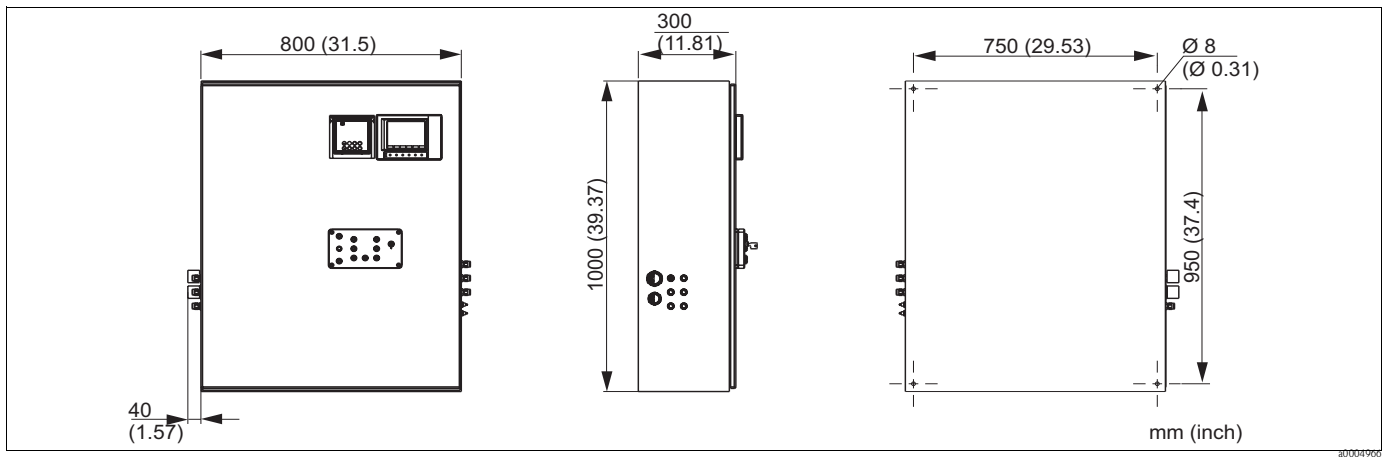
Abmessungen Umschrank CYC310, Kunststoffausführung
